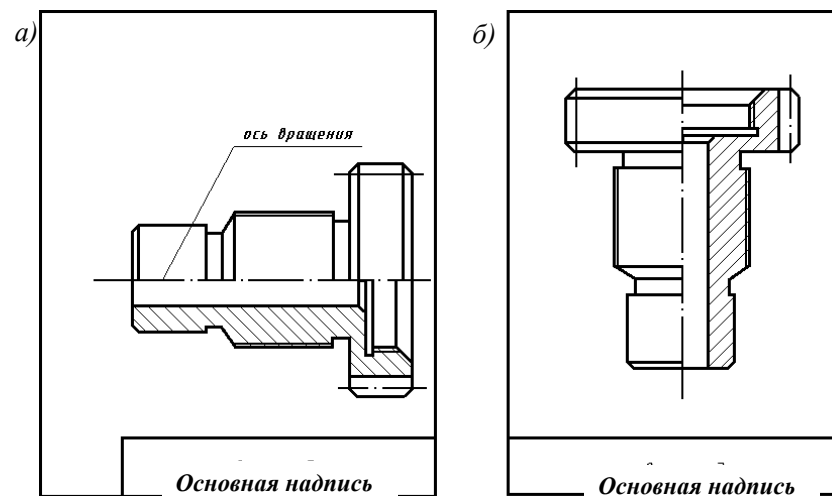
а – горизонтальное расположение вала с зубчатым колесом; б – вертикальное расположение
